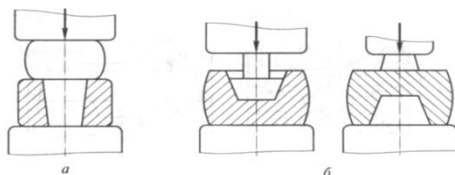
Схемы высадки (*а*) и двусторонней прошивки (*б*)
